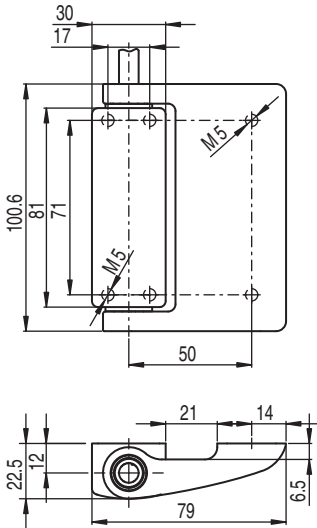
Dimensiones S410-M1CB2-T en mm
